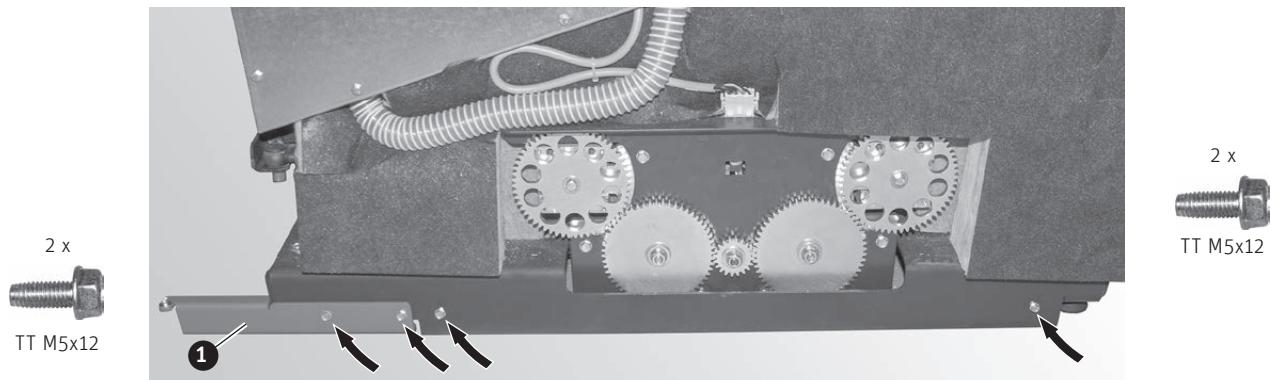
Tür-Befestigungswinkel anschrauben, 2 Schrauben für Verkleidung bis zur Hälfte eindrehen
